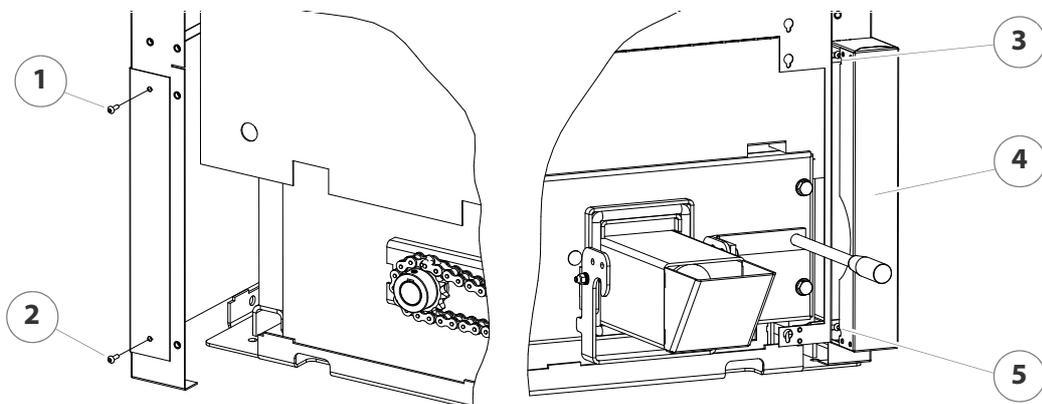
/19 - Montage des jaquettes latéral côté conduit de fumée, en bas
